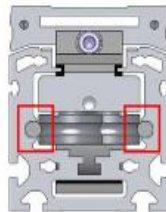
SECCIÓN DE UN MÓDULO LINEAL DE GUÍA DE RODILLOS
